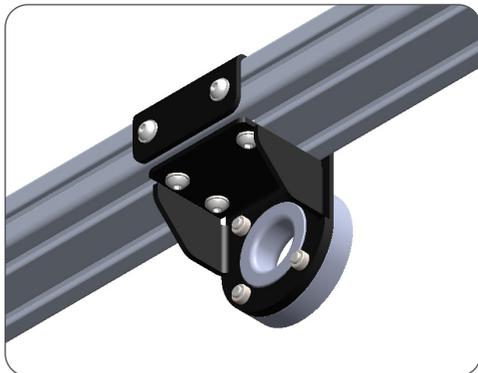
Halter 2.1 von unten/ bracket 2.1 bottom view
